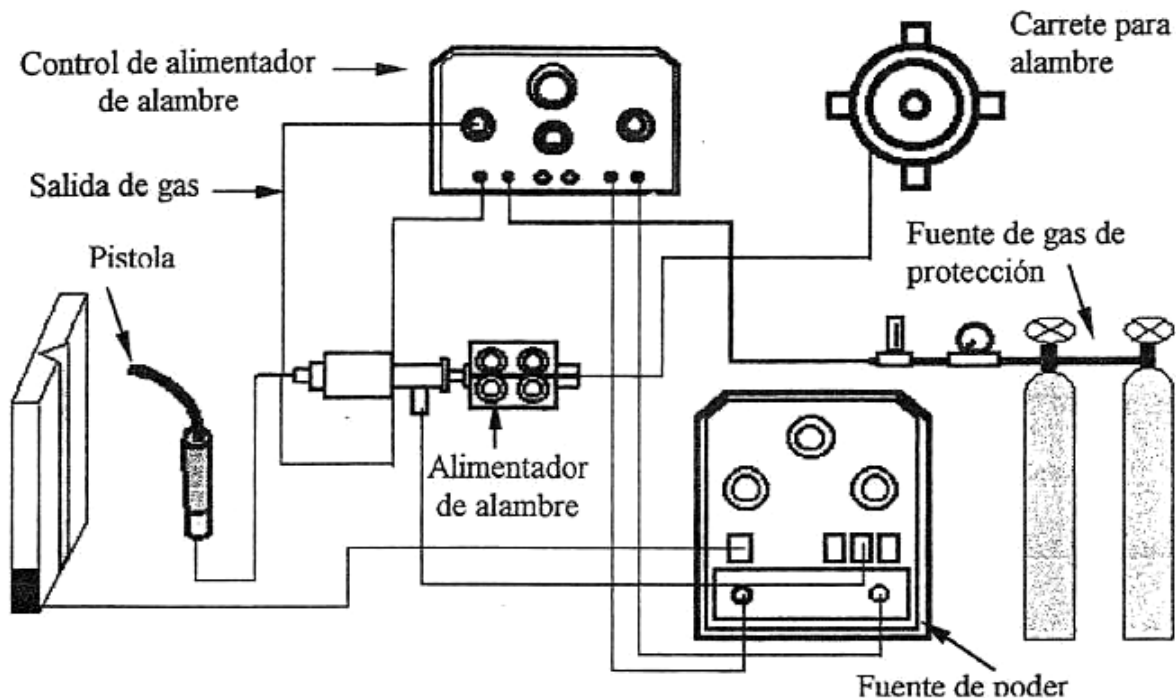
EQUIPO DE PROCESO DE SOLDADURA POR ARCO METÁLICO CON ALAMBRE CONTINUO
